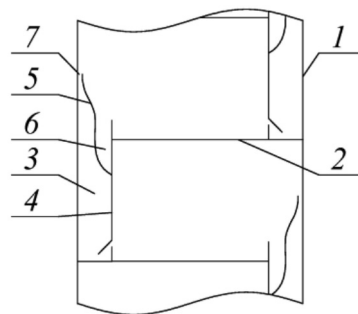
Сегментный корпус переливного устройства с пеноразрушителем [5]:
